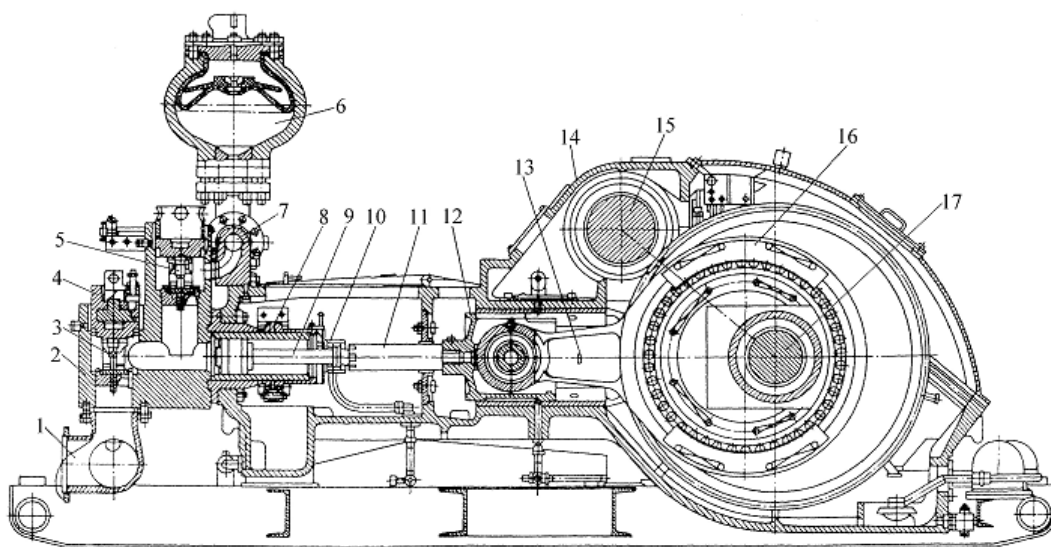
Буровой насос НБТ-600: 1 — всасывающий коллектор; 2 — крышка клапанной коробки; 3, 5 всасывающий и нагнетательный клапаны; 4 — крышка клапана; 6 — пневмокомпенсатор; 7 — нагнетательный коллектор; 8 — цилиндрическая втулка; 9 — шток; 10 — быстроразъемный хомут; 11 — надшток; 12 — крестовина; 13 — шатун 14 — станина насоса; 15 — трансмиссионный вал; 16 — эксцентрик; 17 —
